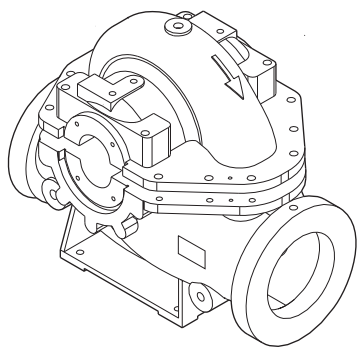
Верхняя и нижняя части корпуса насоса VLS
